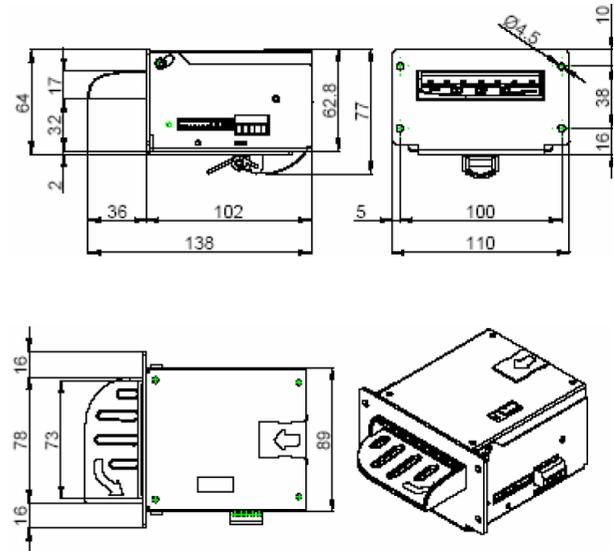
Dimensiones físicas en milímetros del Billetero F30 de EDUE
